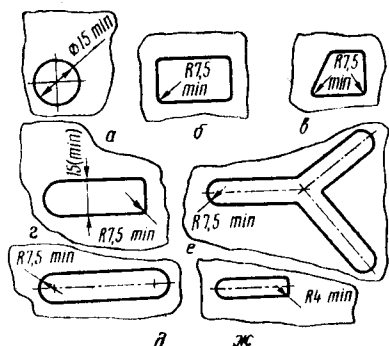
Минимальные размеры отверстий, фрезерованных на фрезерных станках с ЧПУ:
